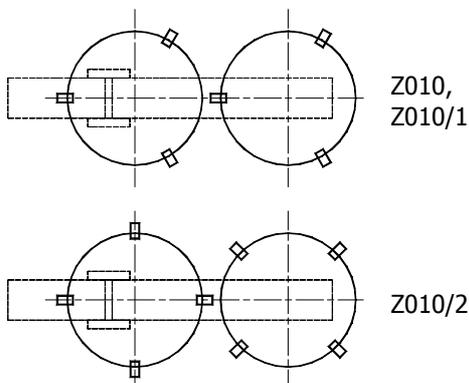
Схема расположения ножей на рабочих тарелках косилки
